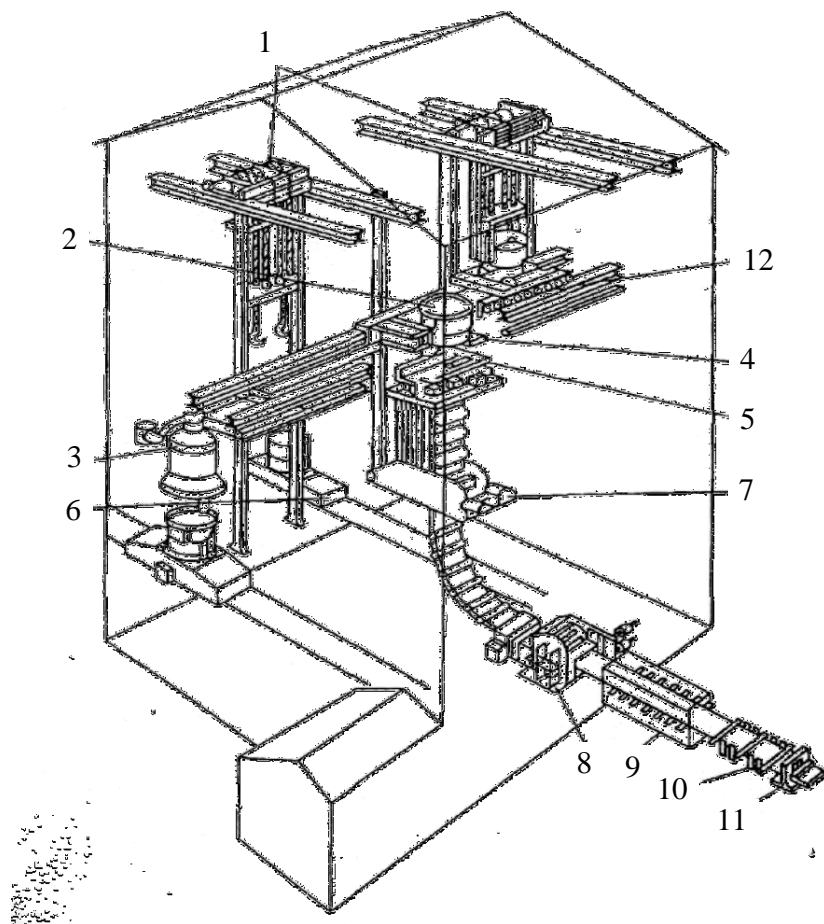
Схема МНЛЗ, совмещённой с прокаткой: 1 – подъемник сталеразливочного ковша; 2 – сталеразливочный ковш; 3 – одна из двух установок вакуумирования; 4 – промежуточный ковш а тележке; 5 – кристаллизатор; 6 – тележка для транспортирования сталеразливочного ковша; 7 – тянущие валки; 8 – правильная машина; 9 – подогревательная печь; 10 – обжимной стан; 11 – газорезка; 12 – разливочная тележка
